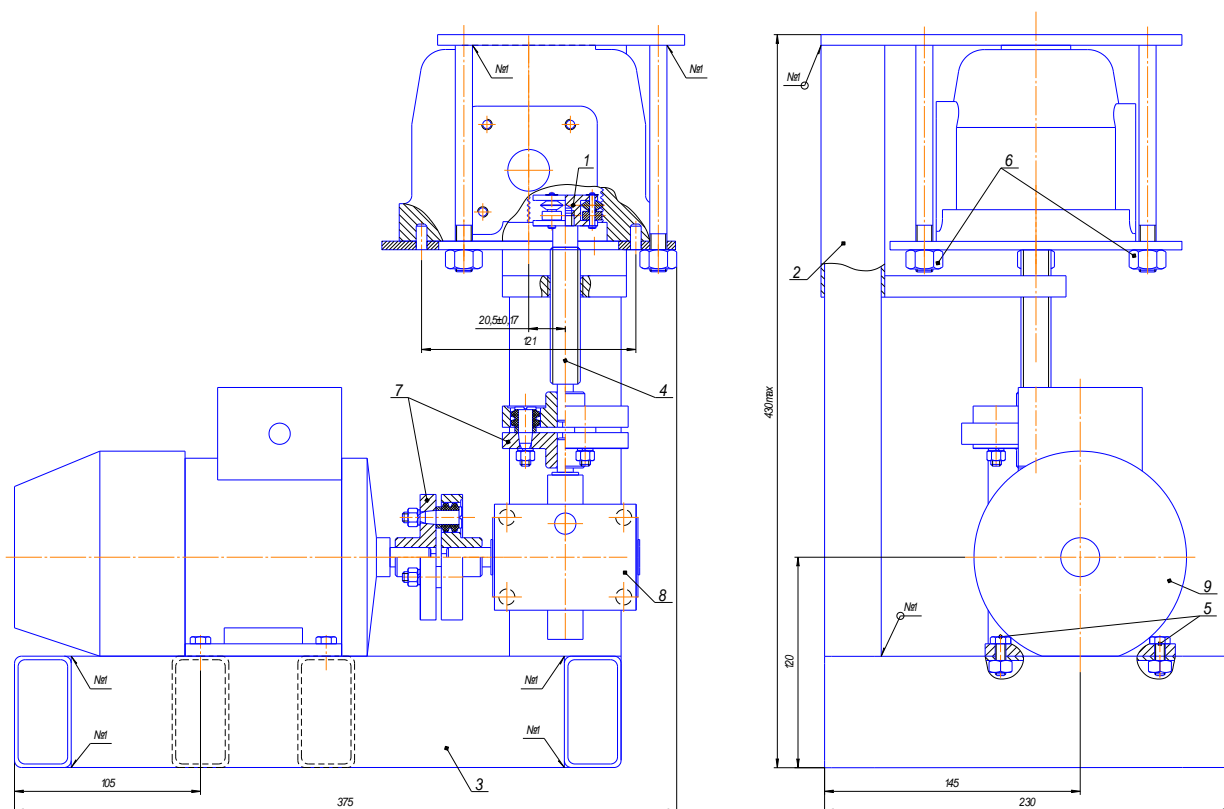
Схема приспособления для ремонта корпусов гидронасосов
